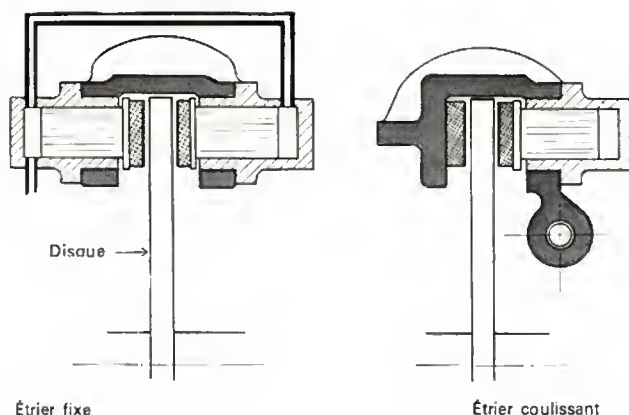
Principe des principaux types d'étriers pour disque fixé axialement
